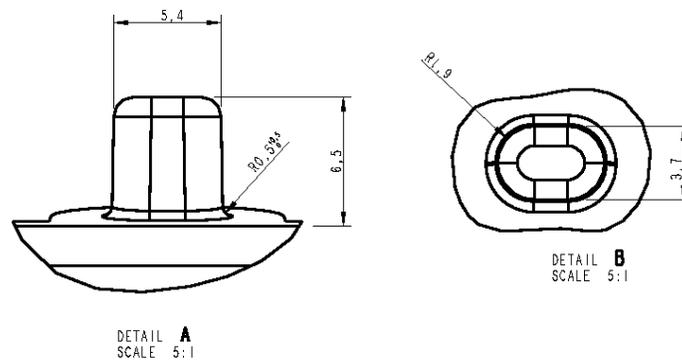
Desenho Conjunto Tampa/Dispenser.
